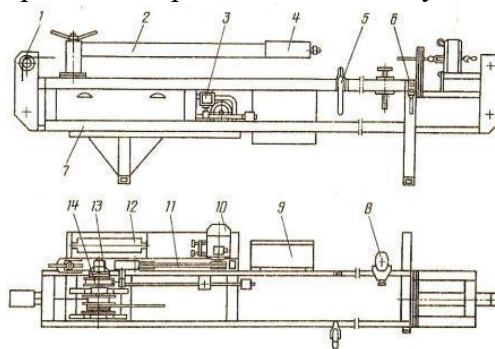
Стенд для правки кожухов шнеков и элеваторов комбайнов: 4) – Поворотная оправка; 6) – Кнопочная станция; 8) – Выдвижная опора; 11) – Клиноремённая передача
